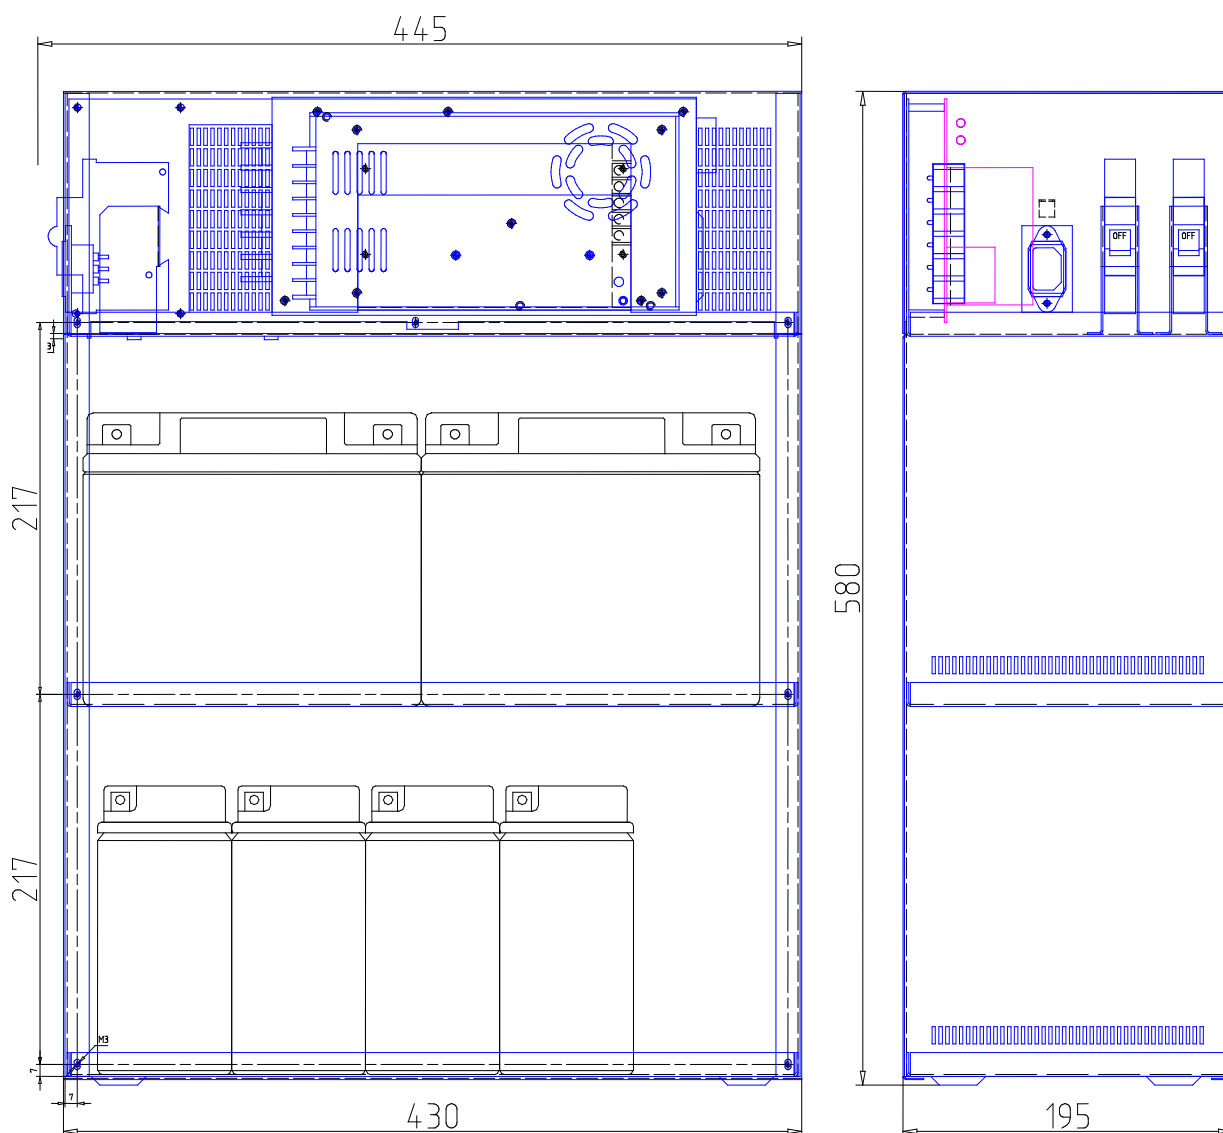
Внешний вид ИБП Штиль PS24 (в корпусе G2). Габаритные размеры
